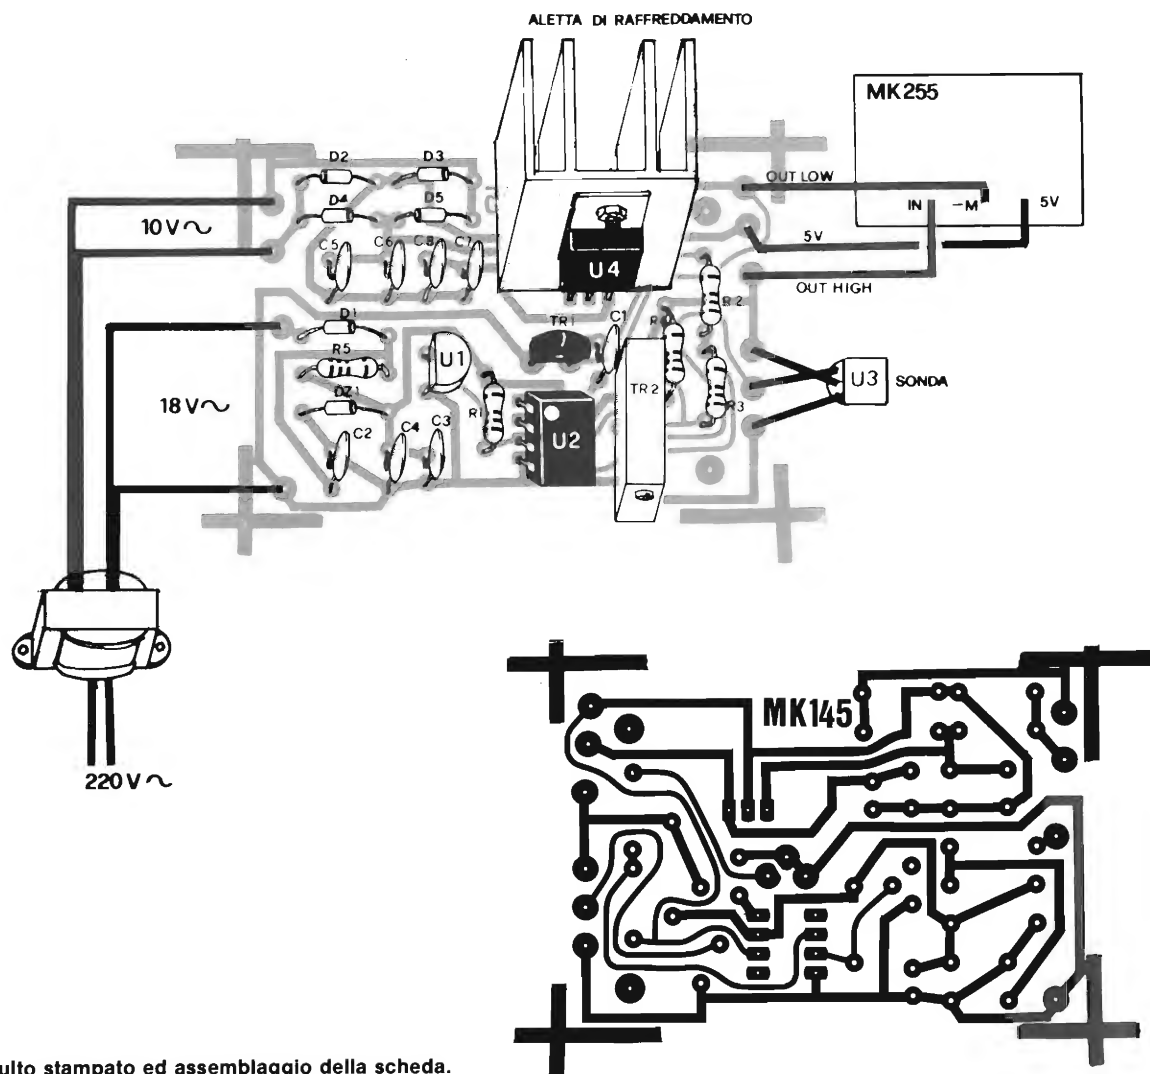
Circuito stampato ed assemblaggio della scheda.
